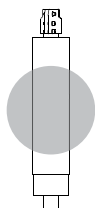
Поместите две защитных трубки на вертикальный приводной вал
